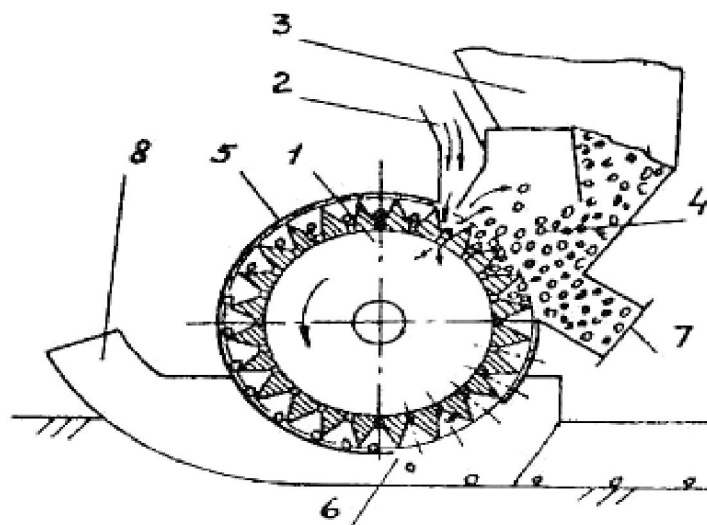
Схема пневматичного висівного апарата сівалки „Аеромат": 1 - висівний диск; 2 - повітряний патрубок; 3 - бункер; 4 - приймальна камера; 5 - обмежувальний щиток; 6 - викидне вікно; 7 розвантажувальний канал; 8 - сошник
